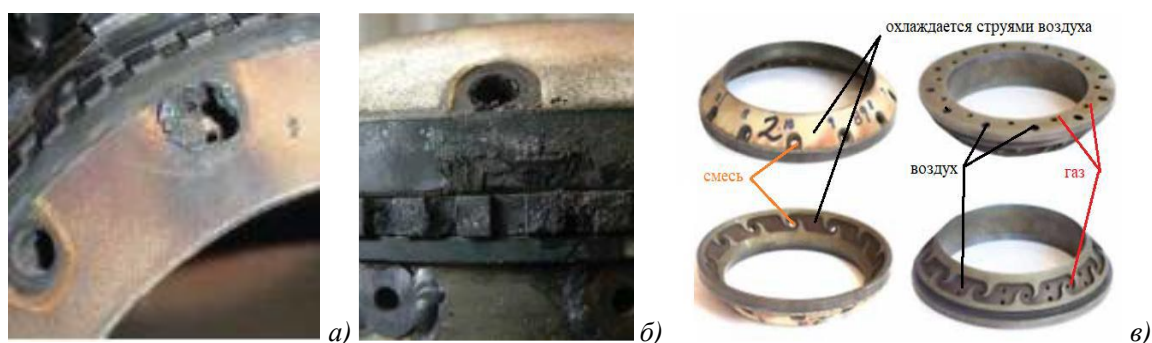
Коррозия отверстия – а; нагар – б; модернизированный торец горелки-в
